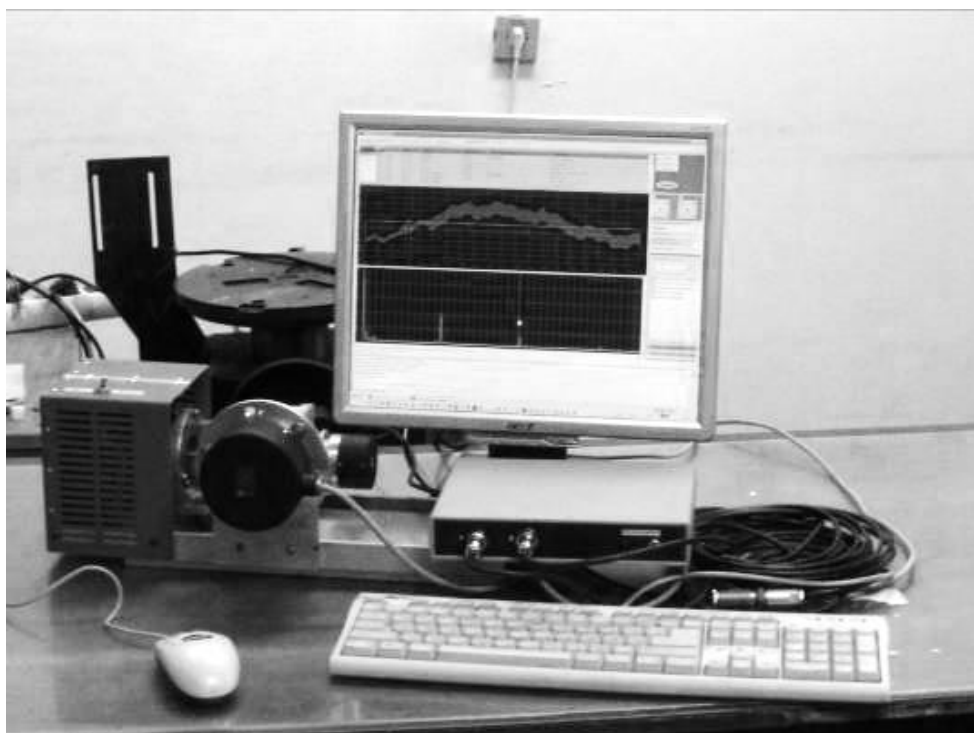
Кинематометр «Диакин-3» при проверке редуктора
